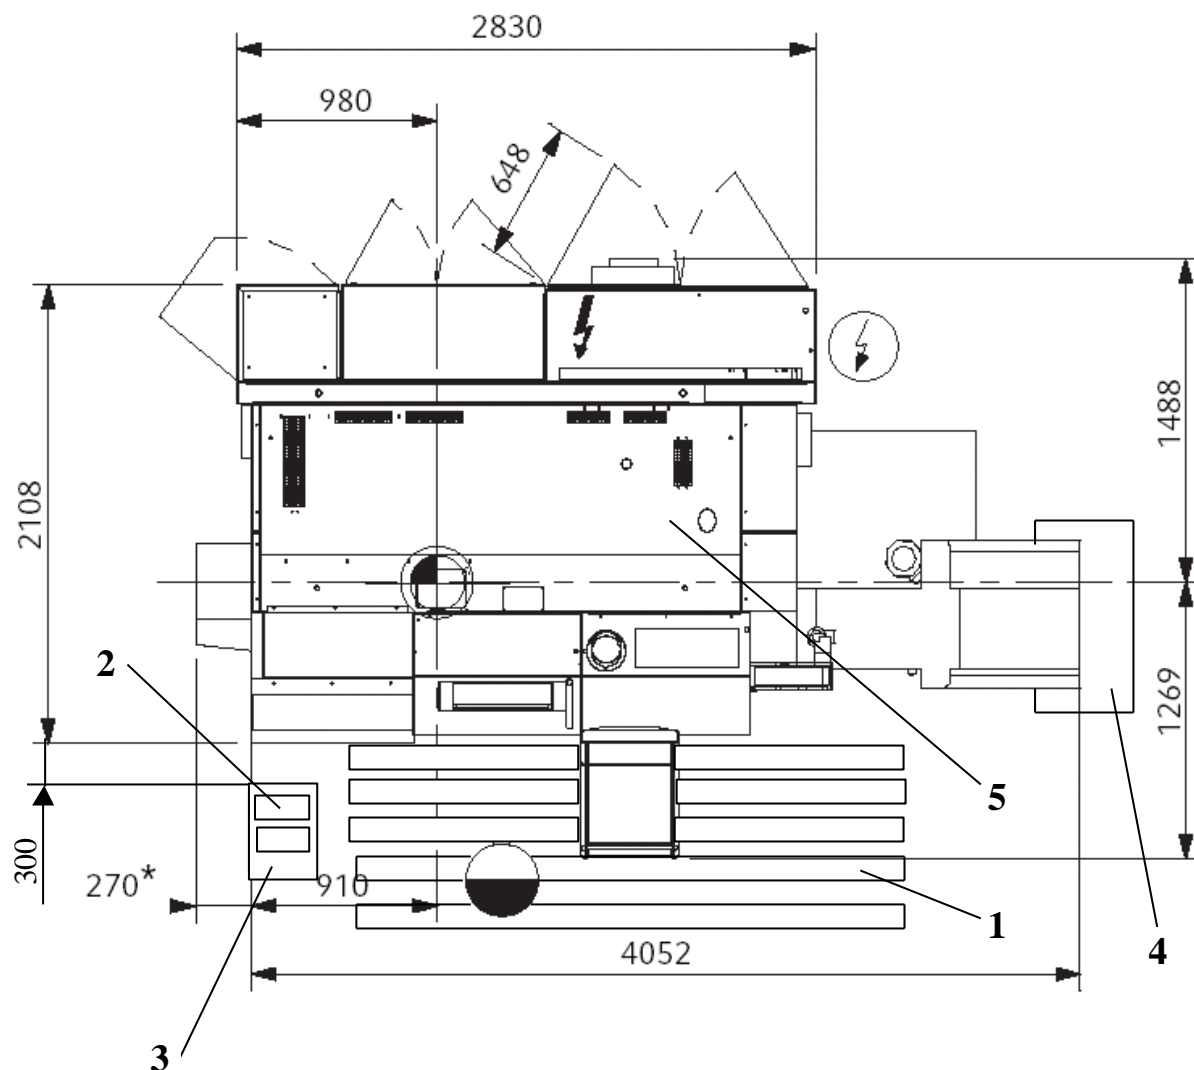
Планування робочого місця оператора токарно-револьверного багатоопераційного верстату з ЧПК:
